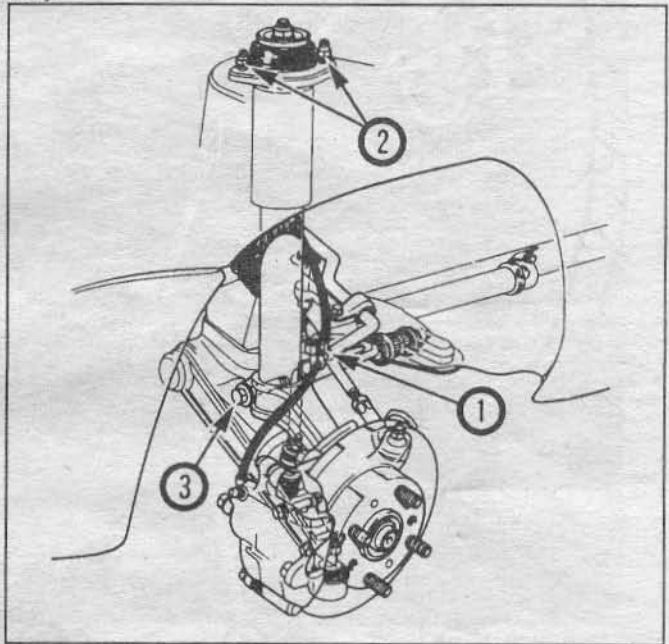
Детали стойки (1984 - 1987 гг.): 1 - кронштейн тормозного шланга; 2 - гайки крепления стойки; 3 - зажимной болт стойки на поворотном кулаке.
